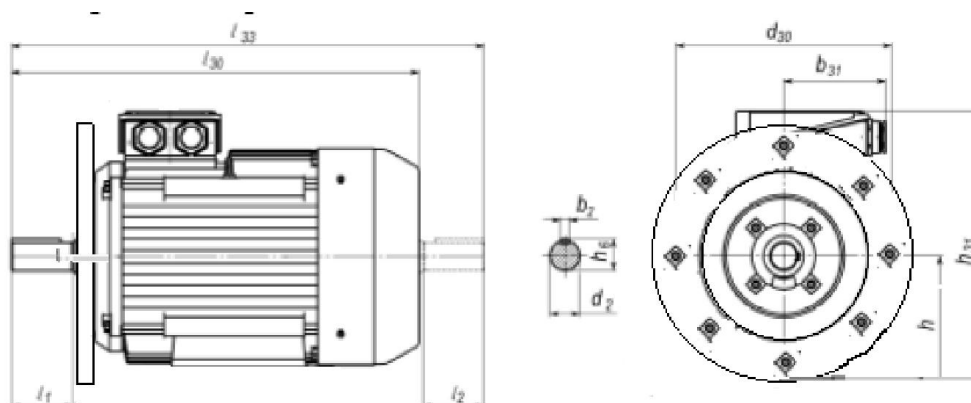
Асинхронный трехфазный двигатель RA180M3.
